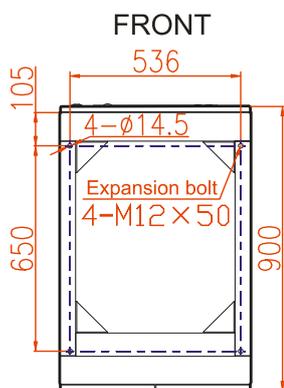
Нижний размер для MR33125 (вид снизу) (мм)
